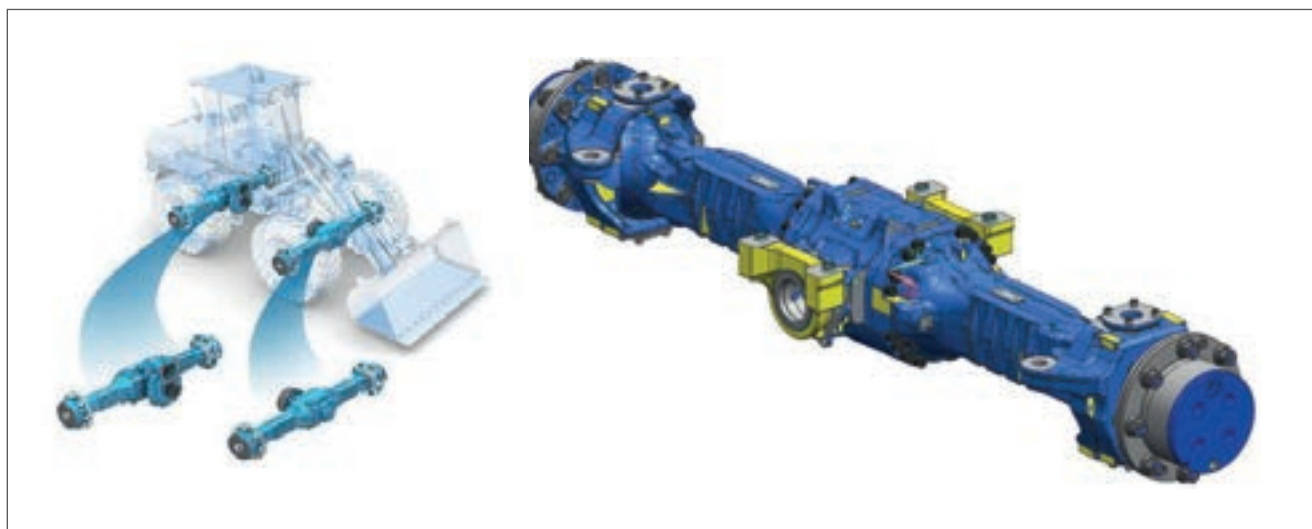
Posizione degli assali in una macchina caricatrice frontale (sinistra) e assale oggetto della tesi (destra).
